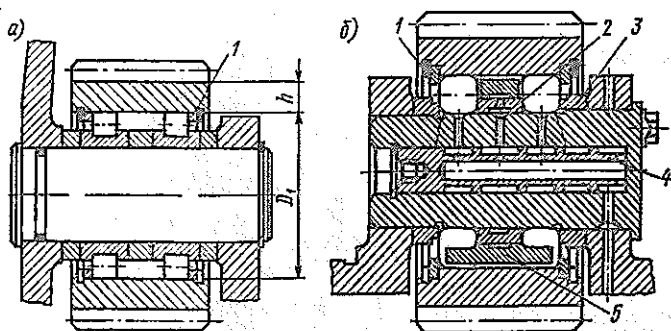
Конструкции узлов сателлитов с нестандартными подшипниками качения в отверстии обода
